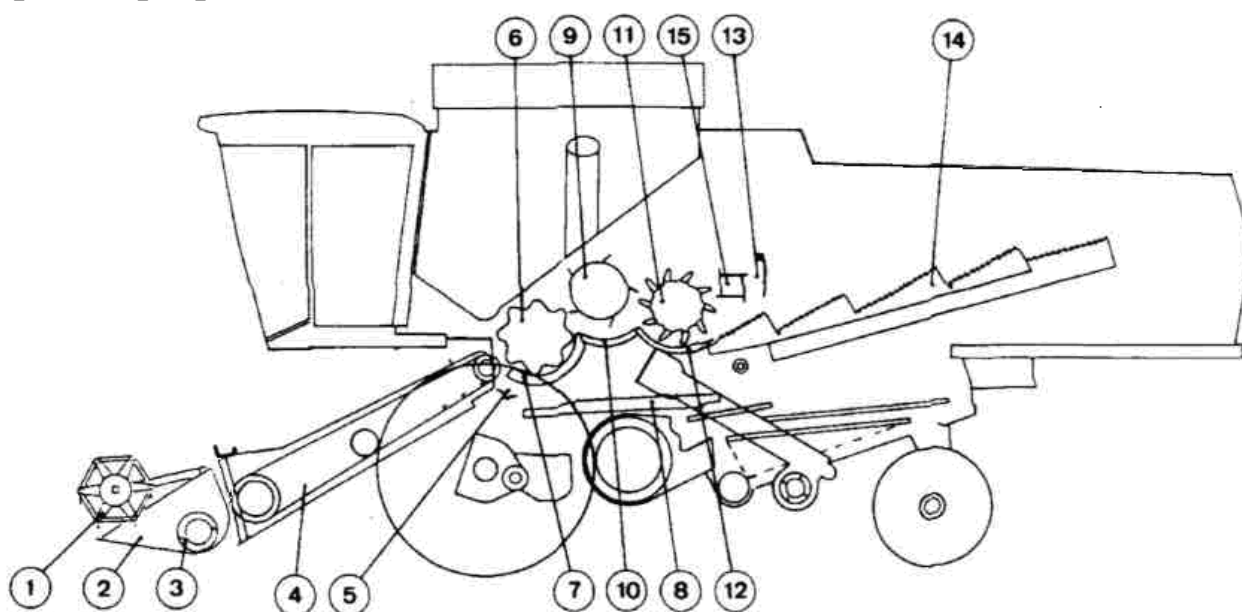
Схема зерноуборочного комбайна New Holland TX-65
